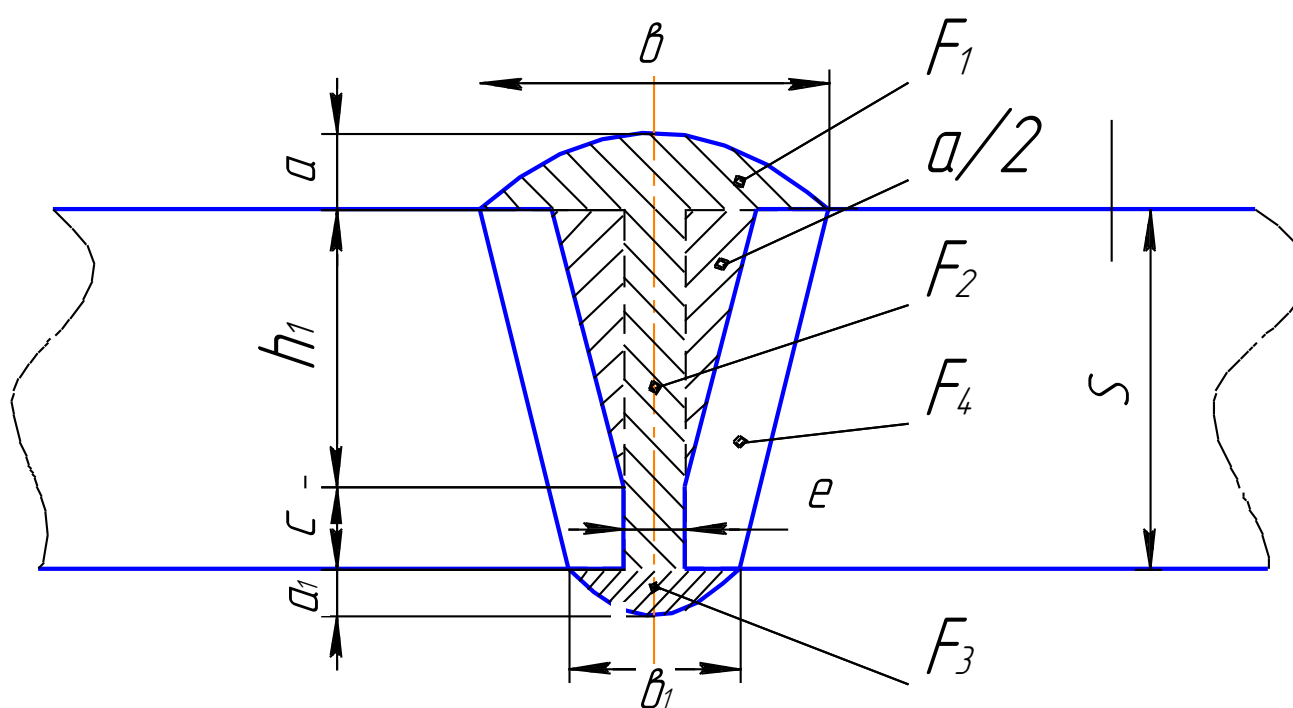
Схема поперечного перерізу балки стикового шва з розробкою кромки
